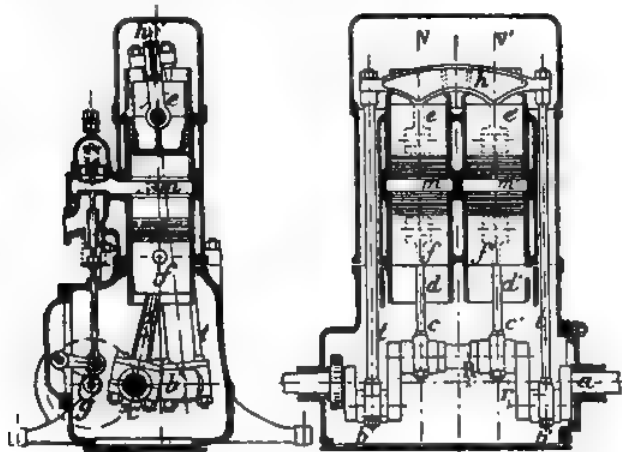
u. 13. Zweizylindriger Motor System Gobron & Brillié.
